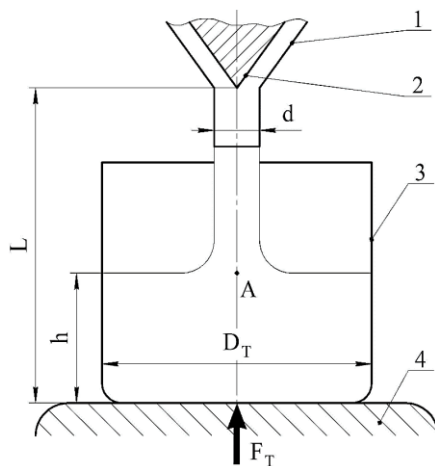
Схема формування дози продукції в тарі циліндричної форми: 1 — фасувальний пристрій; 2 — клапан; 3 — споживча тара; 4 — зважувальний елемент
